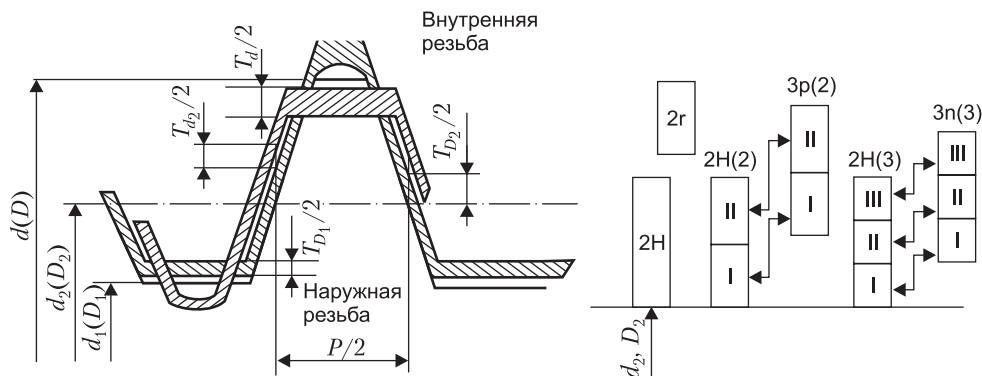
Расположение полей допусков резьбы с натягом
